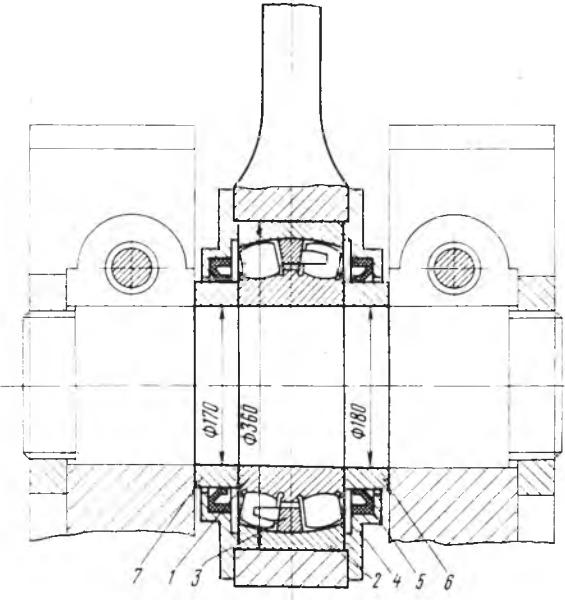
Конструкция подшипникового узла шатунного роликоподшипника:
